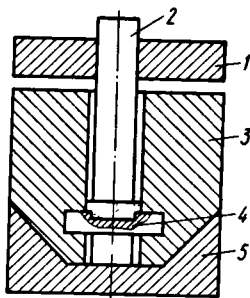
Приспособление для совмещения операций прессования керамики и сварки ее с металлом:
